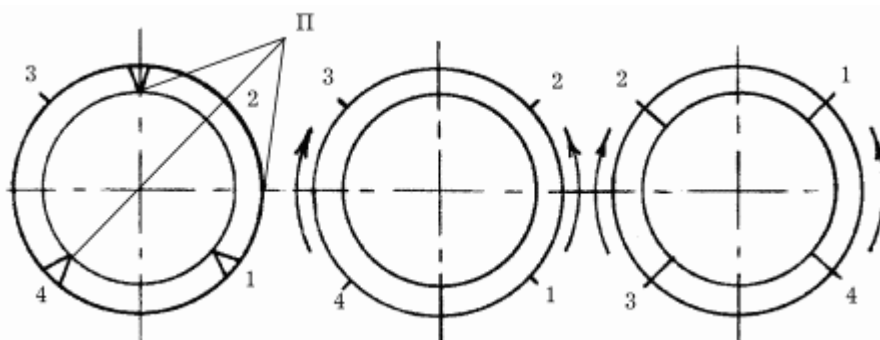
Последовательность сварки поворотных стыков.
